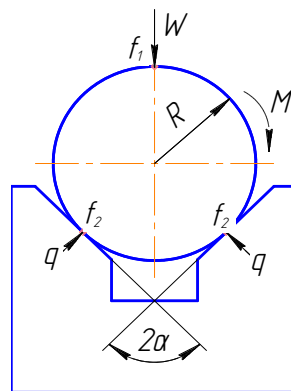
Схема базування заготовки в пристосуванні
